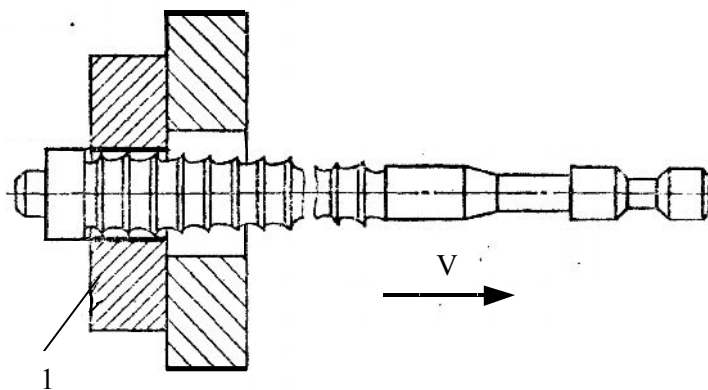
Обработка отверстия протяжкой круглого сечения: 1 – обрабатываемая деталь
